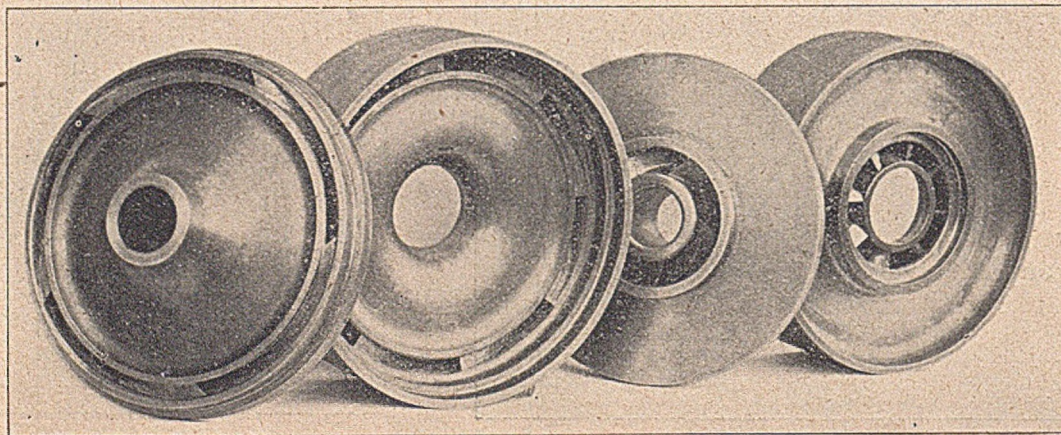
Leit- und Schaufelräder der Hochdruckzentrifugalpumpe, Patent Kugel-Gelpke. In der Ausführung von Escher, Wyfs & Co. in Zürich.
